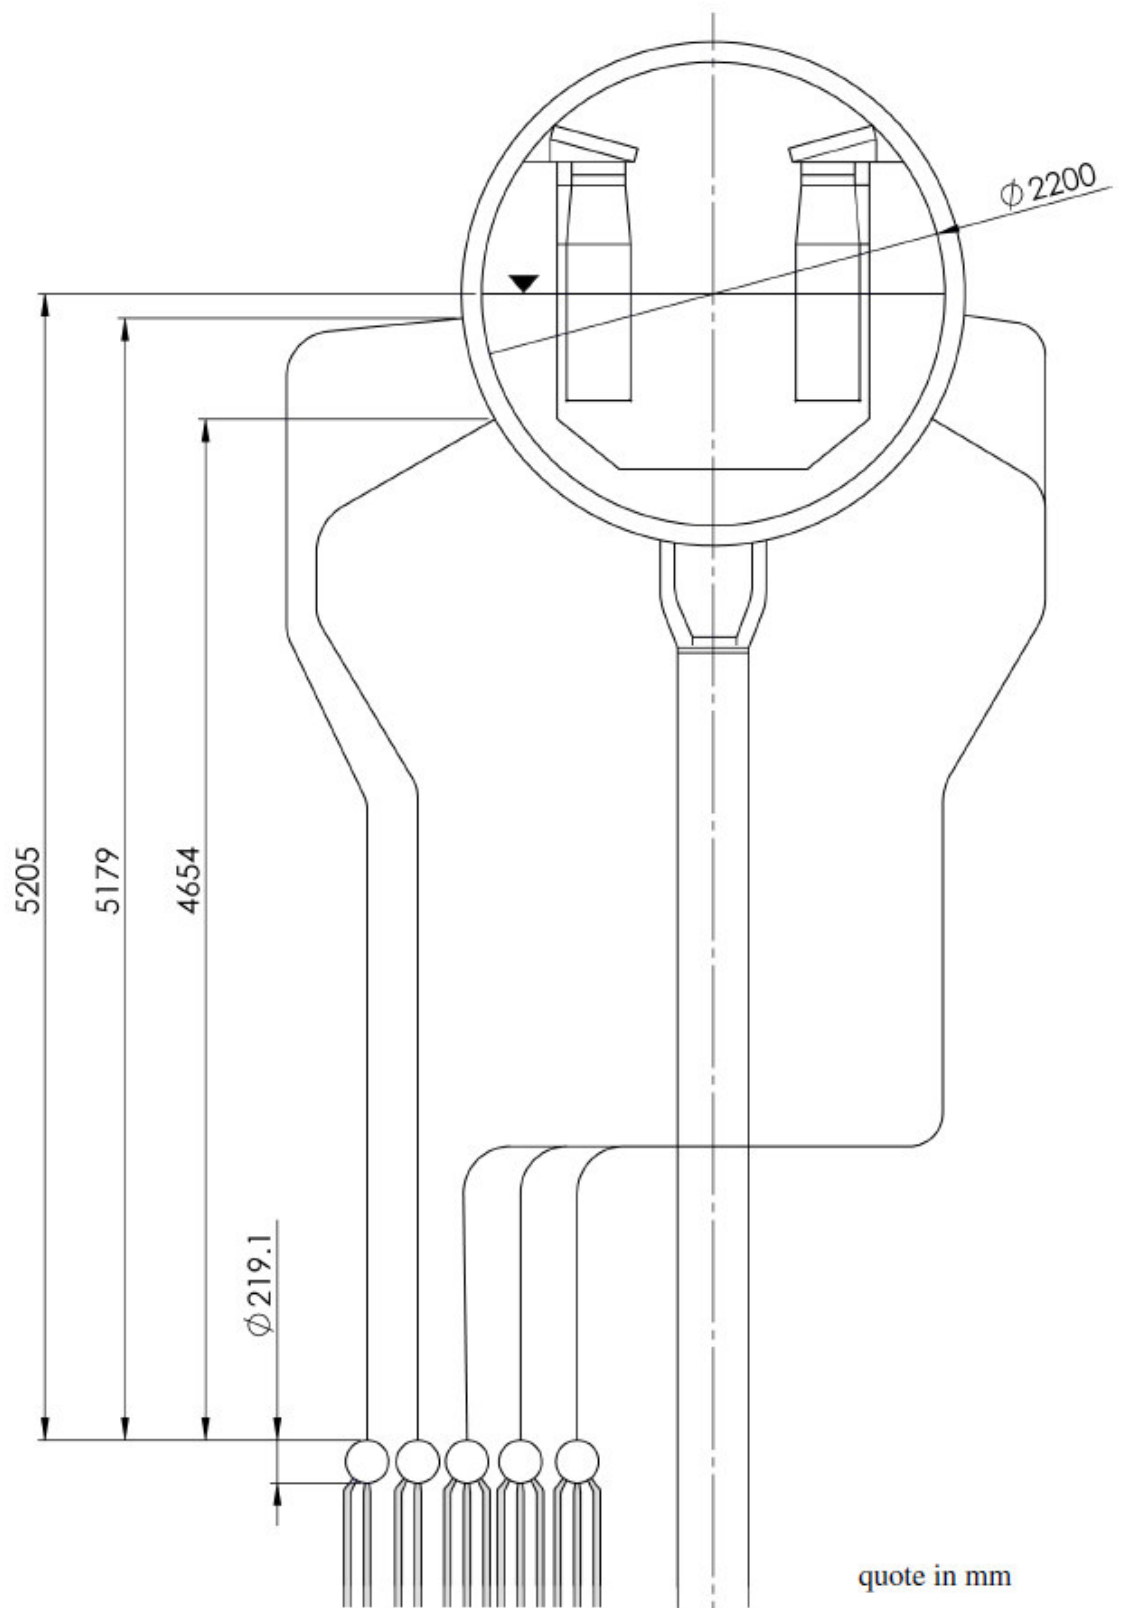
Corpo cilindrico , tubi di caduta e riser.
